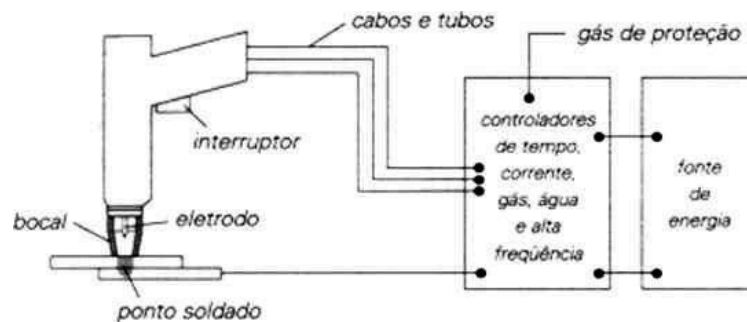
Diagrama de um processo de soldagem TIG pulsado.
